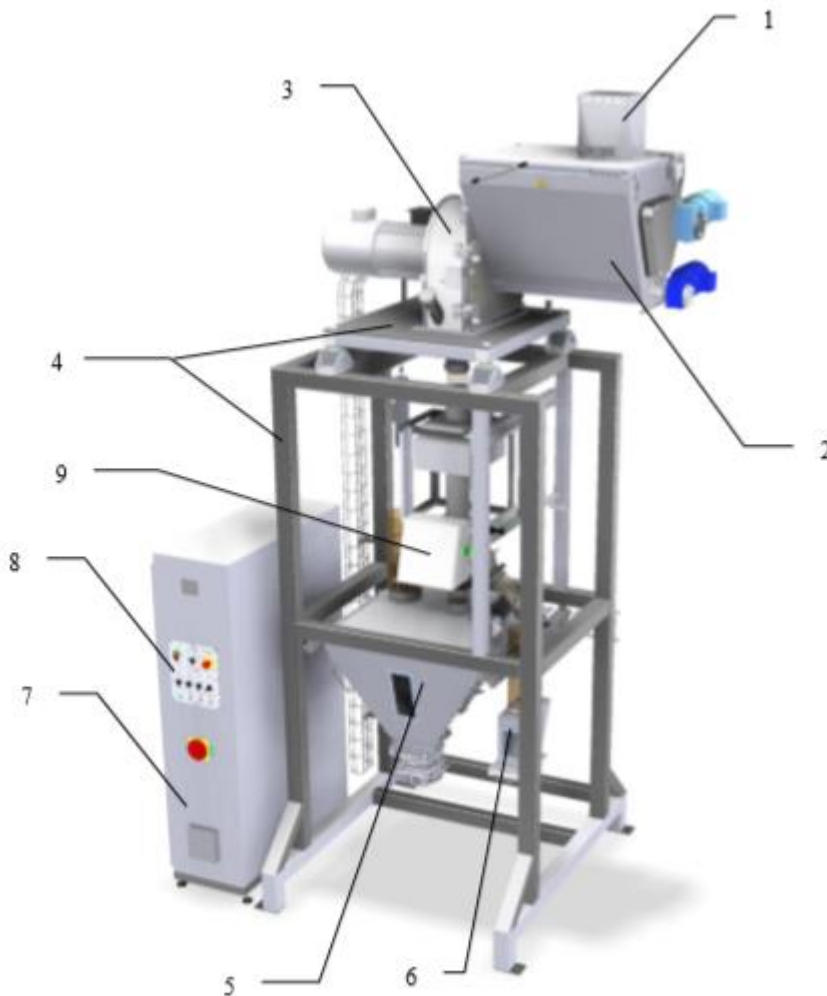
Основні частини роторного подрібнювача РП-3:1) загрузочний патрубок; 2) бункер з валами змішування; 3) подрібнювач з механізмами; 4) рама подрібнювача з платформою; 5) буферний бункер для готового продукту с шибером; 6) смінь для браку; 7) шафа управління; 8) панель управління; 9) металошукач.
